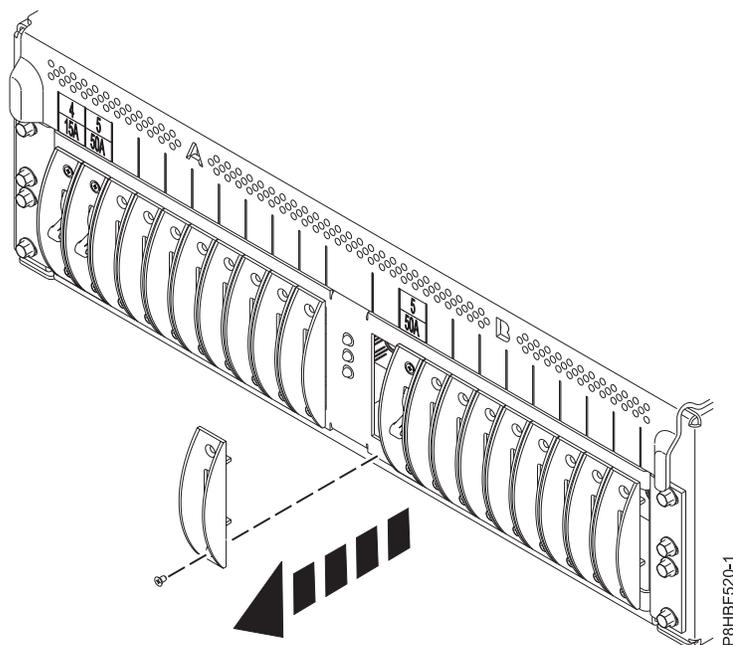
Tampa do disjuntor (a posição mostrada do disjuntor é apenas para referência)
